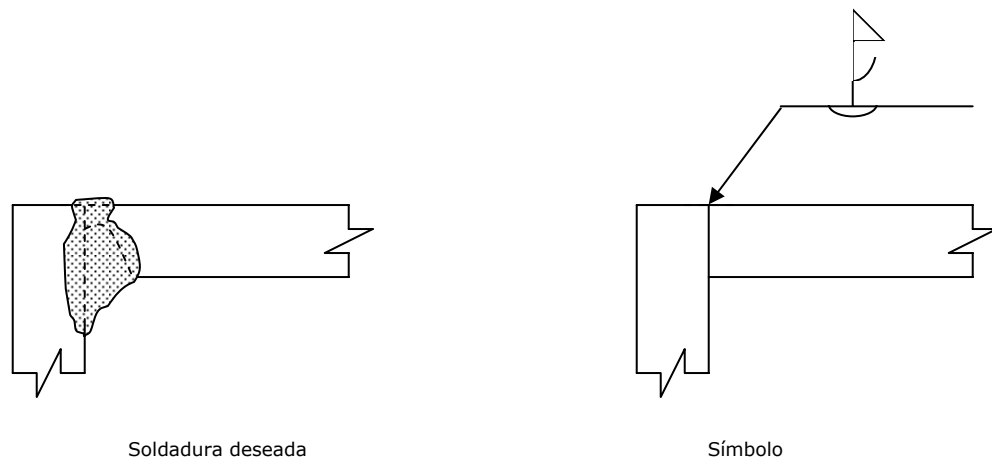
Símbolo de soldadura combinada
